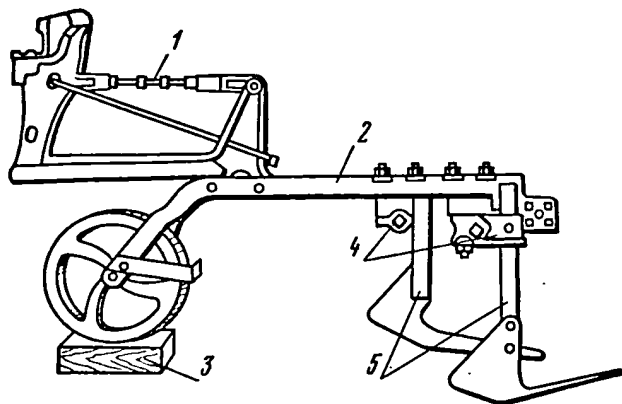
Схема установки рабочих органов культиватора на глубину обработки
